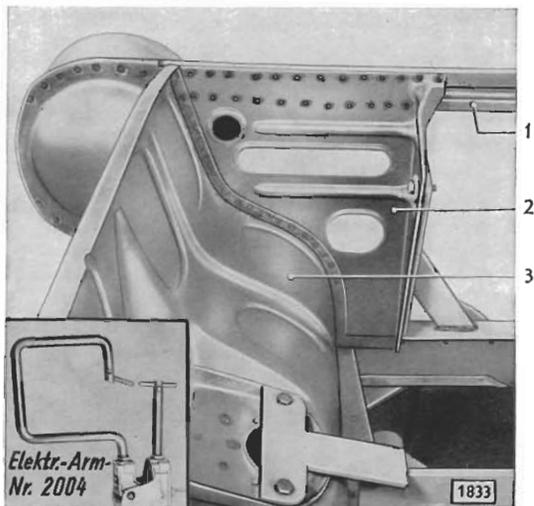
Oberes Luftleitblech an linkes seitliches Luftleitblech im Motorraum punktgeschweißt – auf rechter Wagenseite in gleicher Weise punktschweißen
